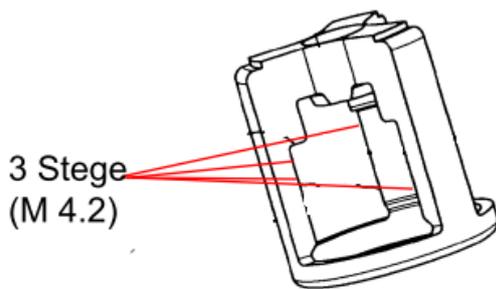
der D3 (freigestellt mit nachgetragenen Merkmalen)
